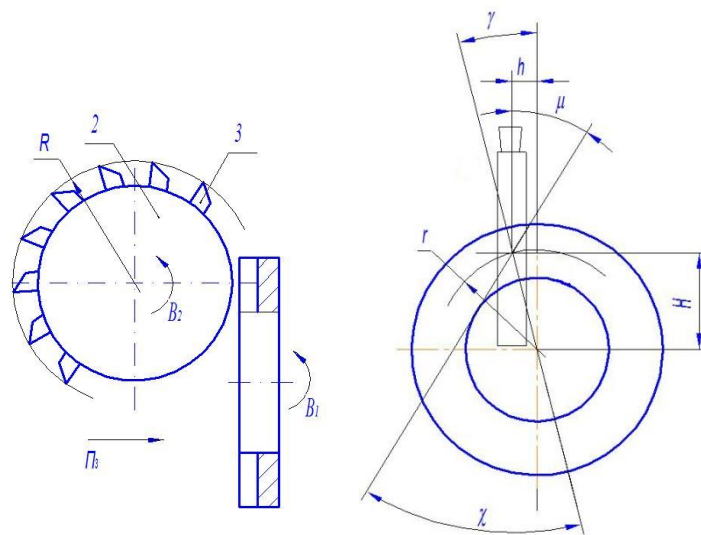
Схема формообразования поверхностей с зубчатым контуром
